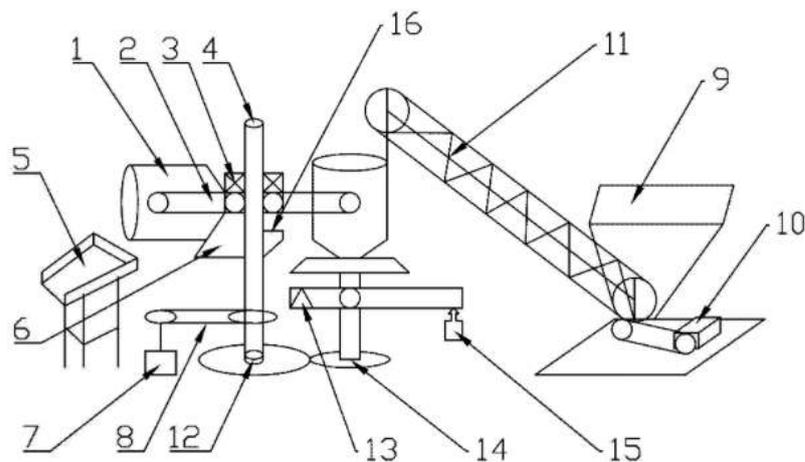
Paddy rice ration packing machine (CN103287599A). Fuente: Chen Feng; Liu Qihua; Ru Yi; Ma Jiaqing; Xu Jiandi; Zhu Wenyin; Zhou Xuebiao; Sun Gongchen; Zhao Qinglei; Gao Jie; Chen Bocong; Wang Yu, (2013)
